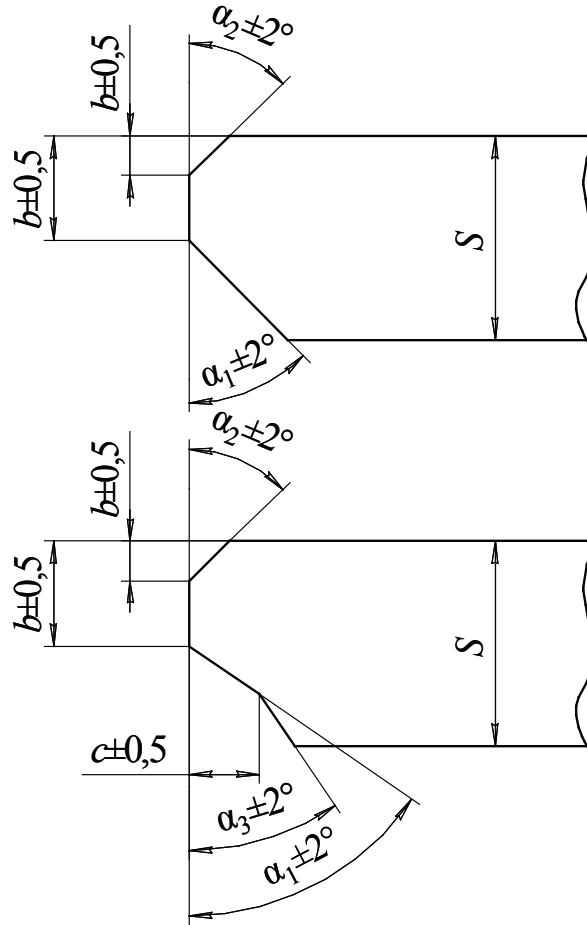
Варианты обработки продольных кромок листовой заготовки
